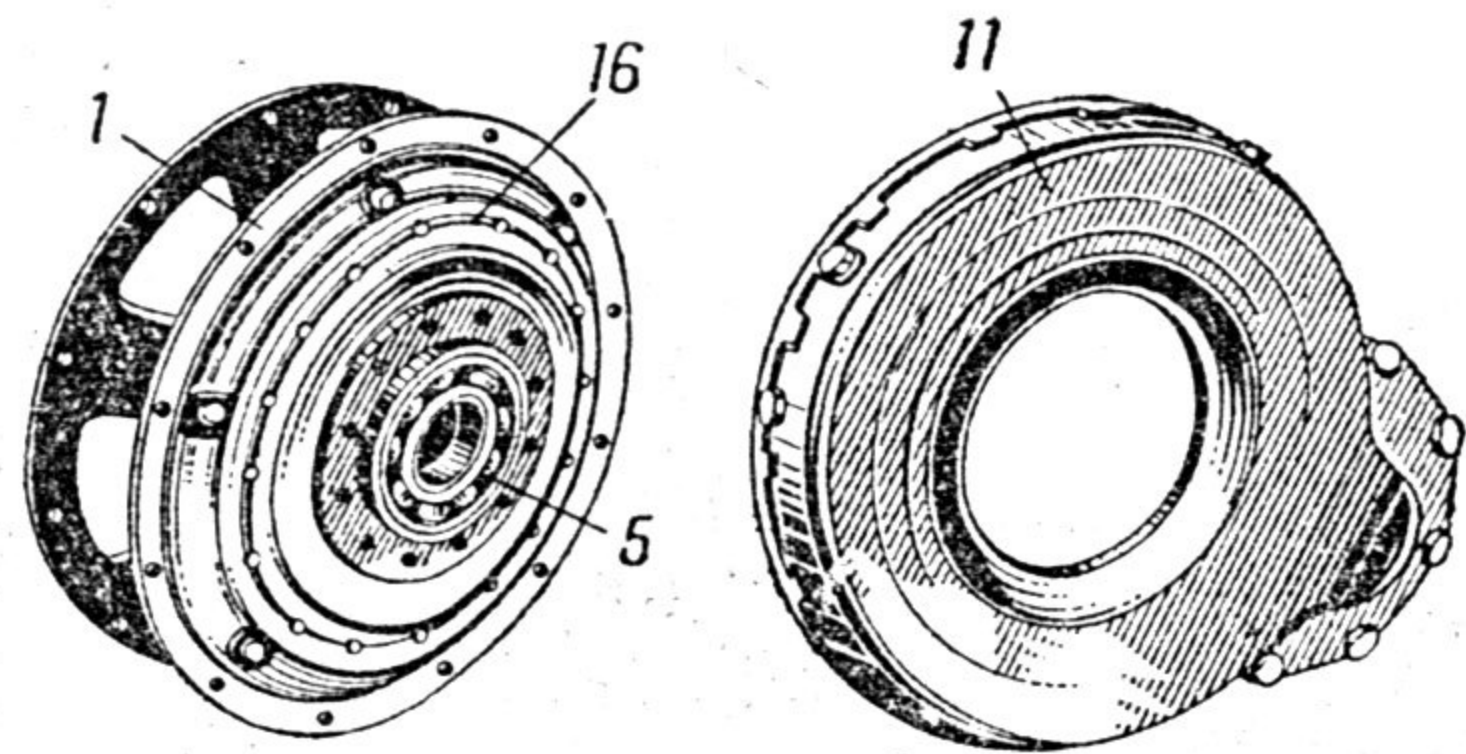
Корпус ведущего колеса с картером бортовой передачи:
